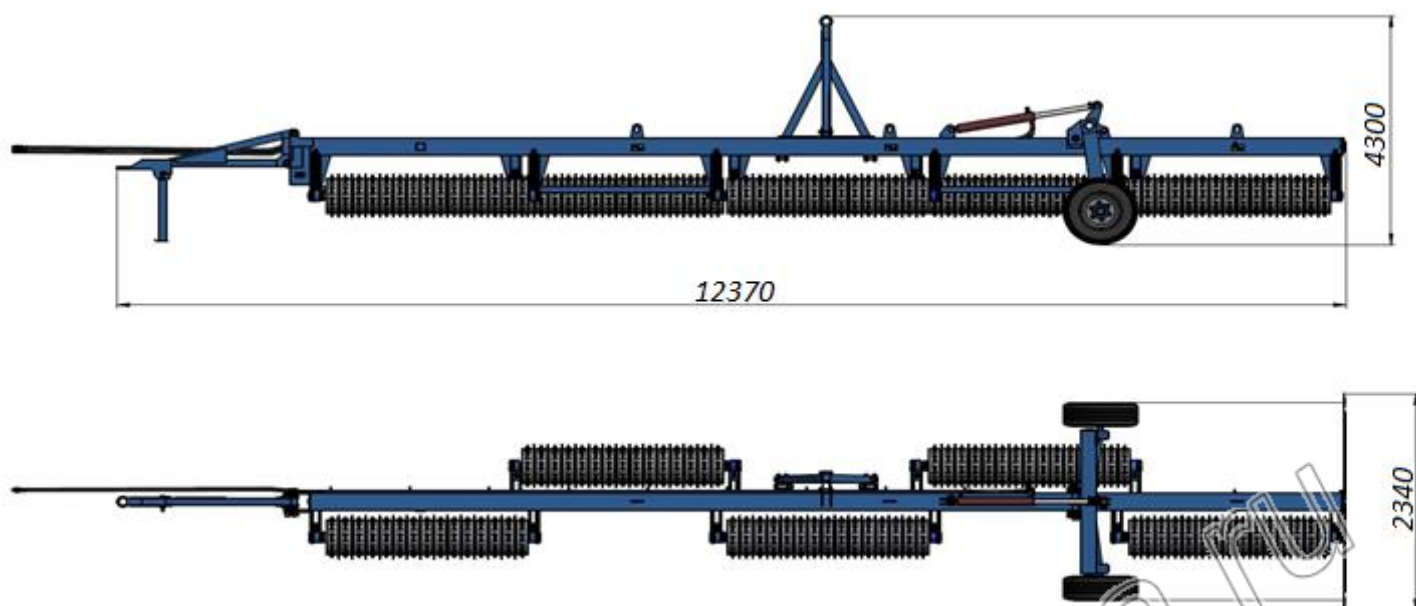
Габаритные размеры в транспортном положении КЗК-10У.
